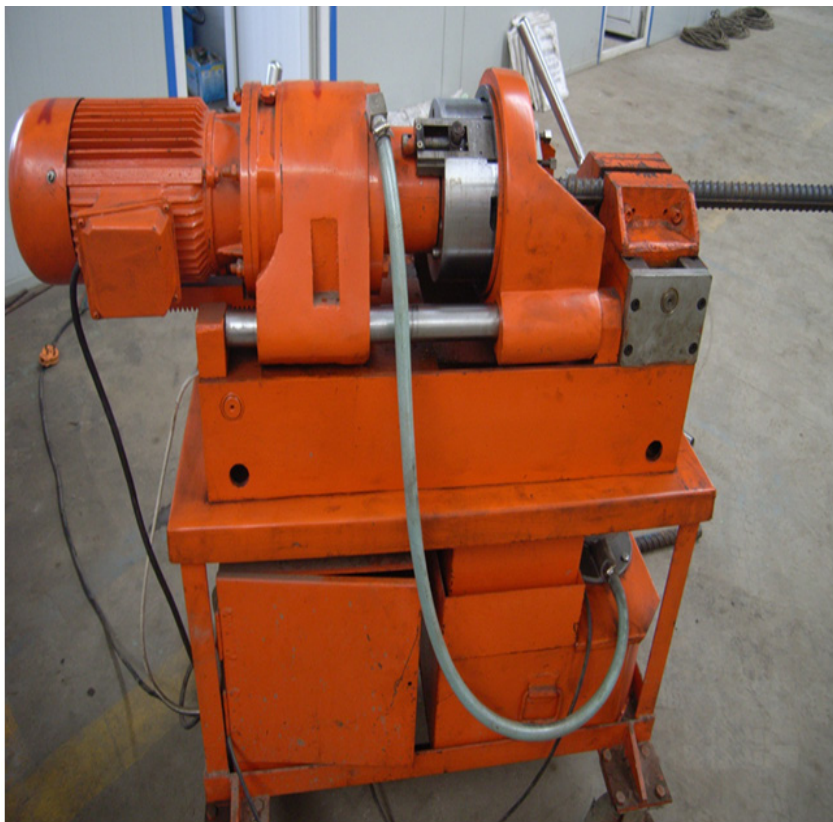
Станок для нарезания конической резьбы на строительной арматуре
